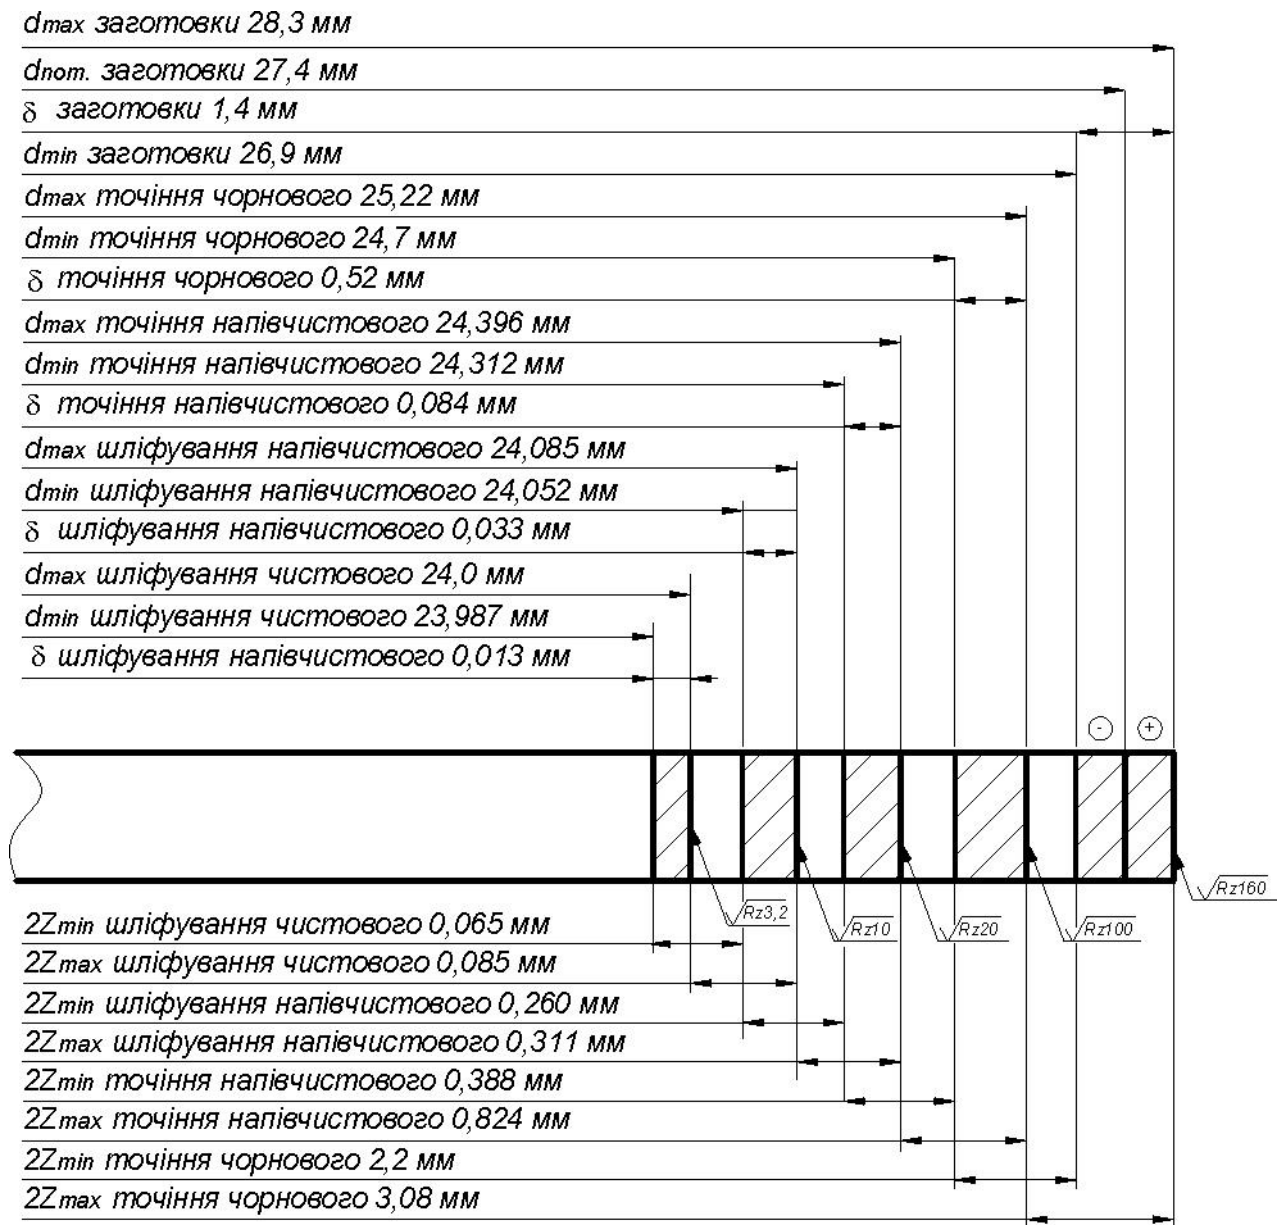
Схема розташування припусків та допусків для поверхні $\varnothing 24h6$
